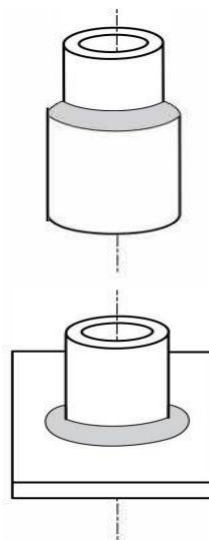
10 Flat Welding Test Position 1F⁹
